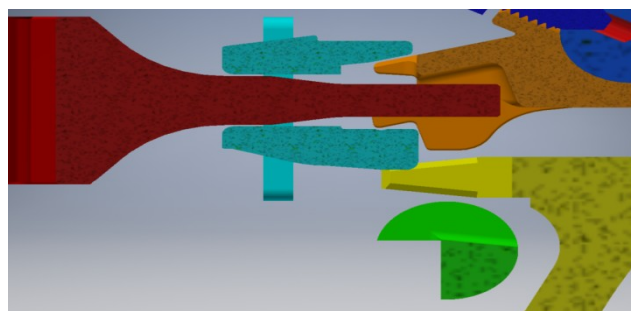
Řazení zpátečky a 1. převodového stupně [autor]
